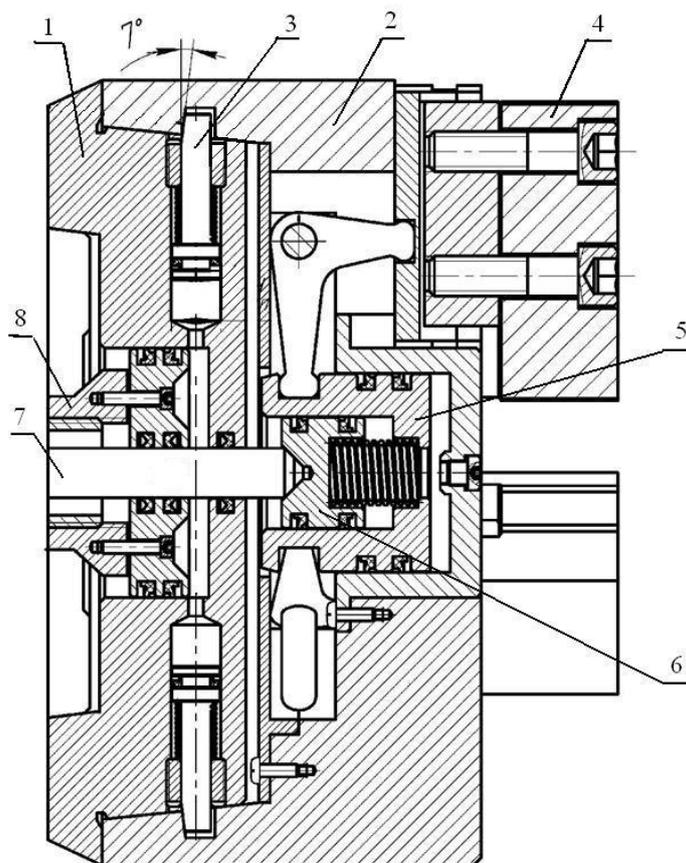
Патрон токарный с гидропластмассовыми устройствами закрепления наладки и заготовки
